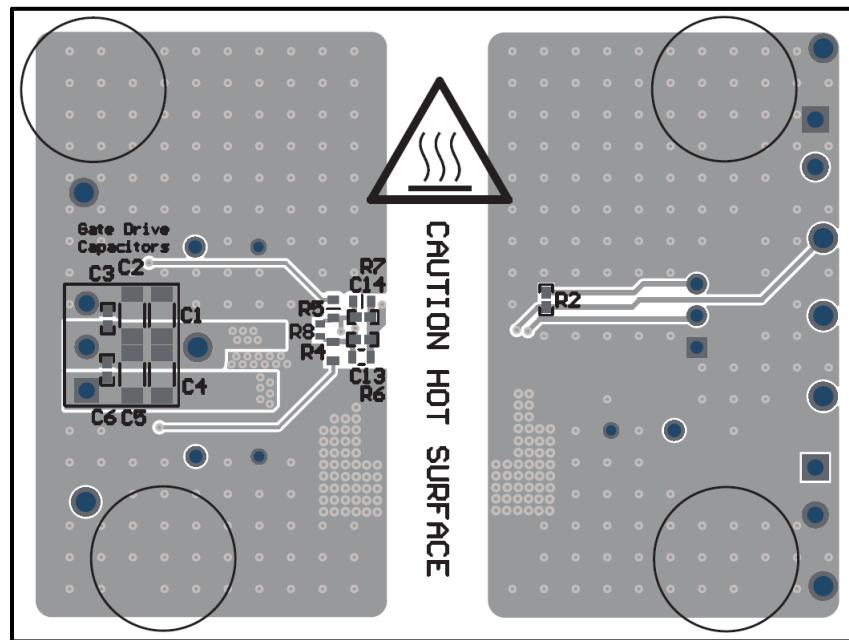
UCC14131EVM-070 , PCB 底层 , 组装 ( 镜像视图 )
